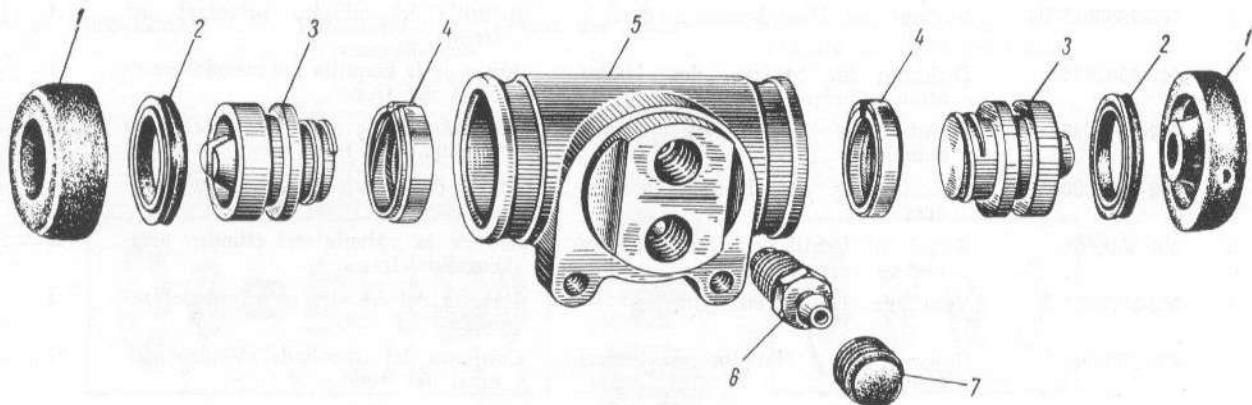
Hydraulischer Radbremszylinder des Hinterrades
